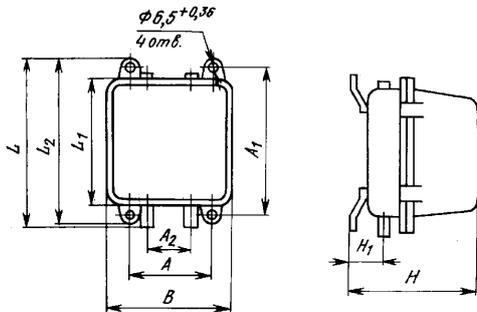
Габаритные, установочные размеры пускателей реверсивных типов ПМ12-080, ПМ12-100, ПМ12-160 степени защиты IP54
